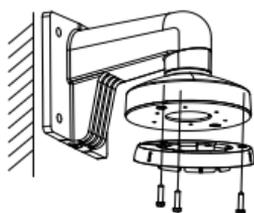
Установка монтажного основания на кронштейн для установки на стену
